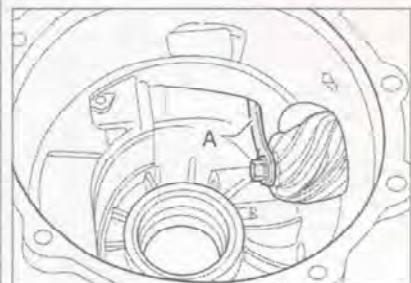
Если ведущая шестерня главной передачи прокручивается, зафиксируйте ее держателем T30051 (A).
